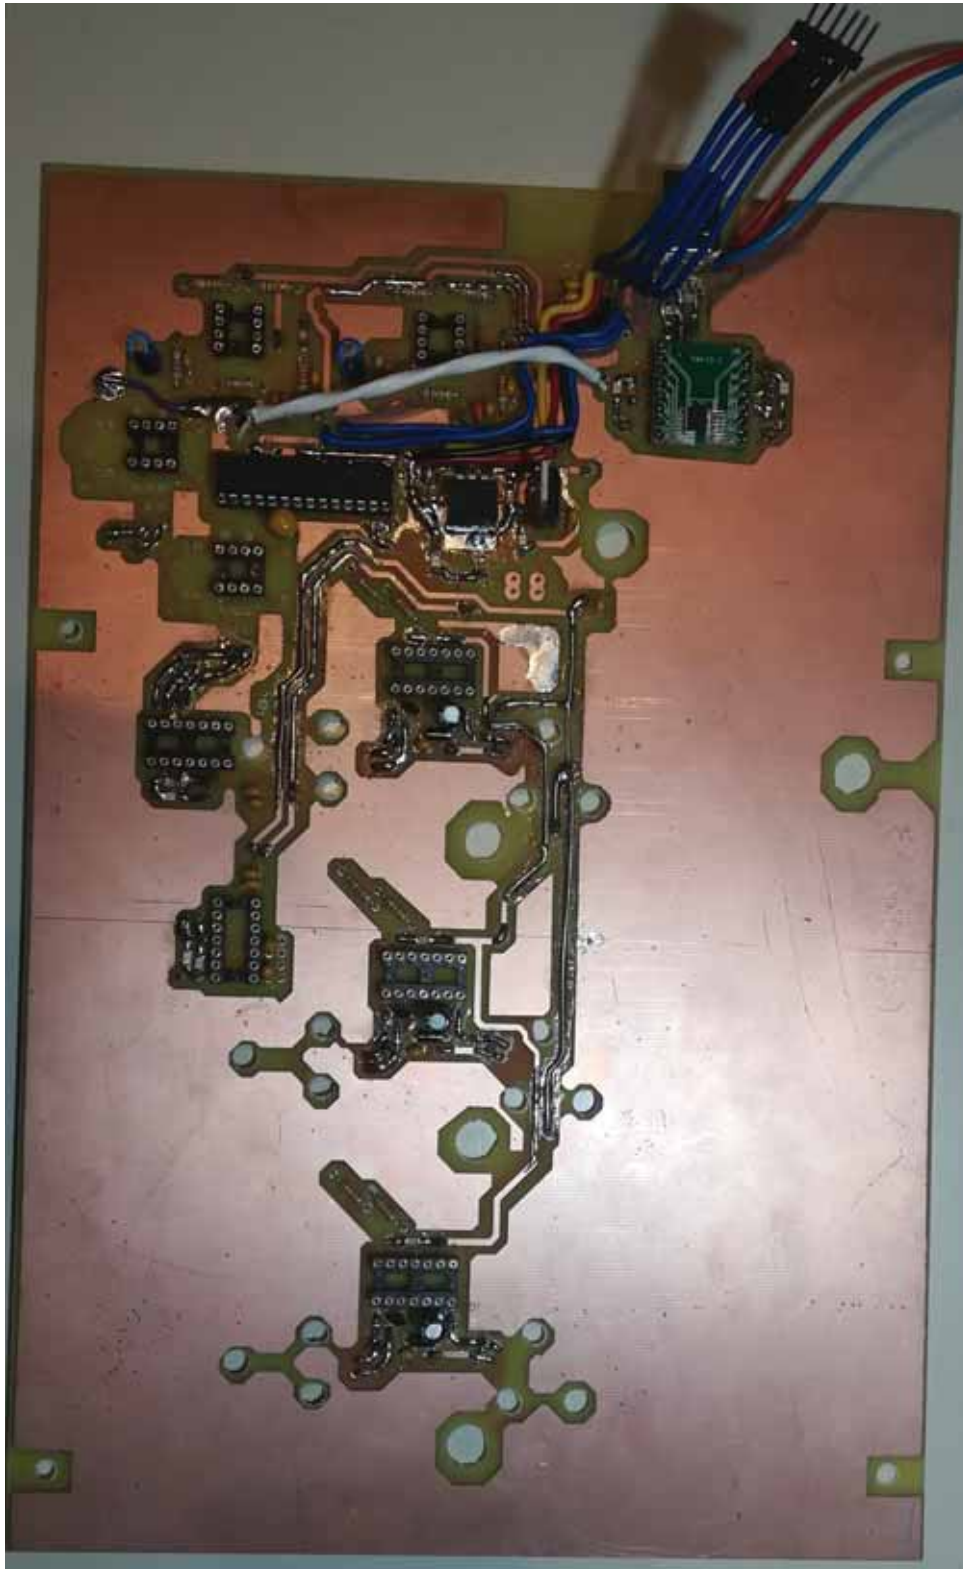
Imagen de la placa superior con todas las soldaduras hechas.
